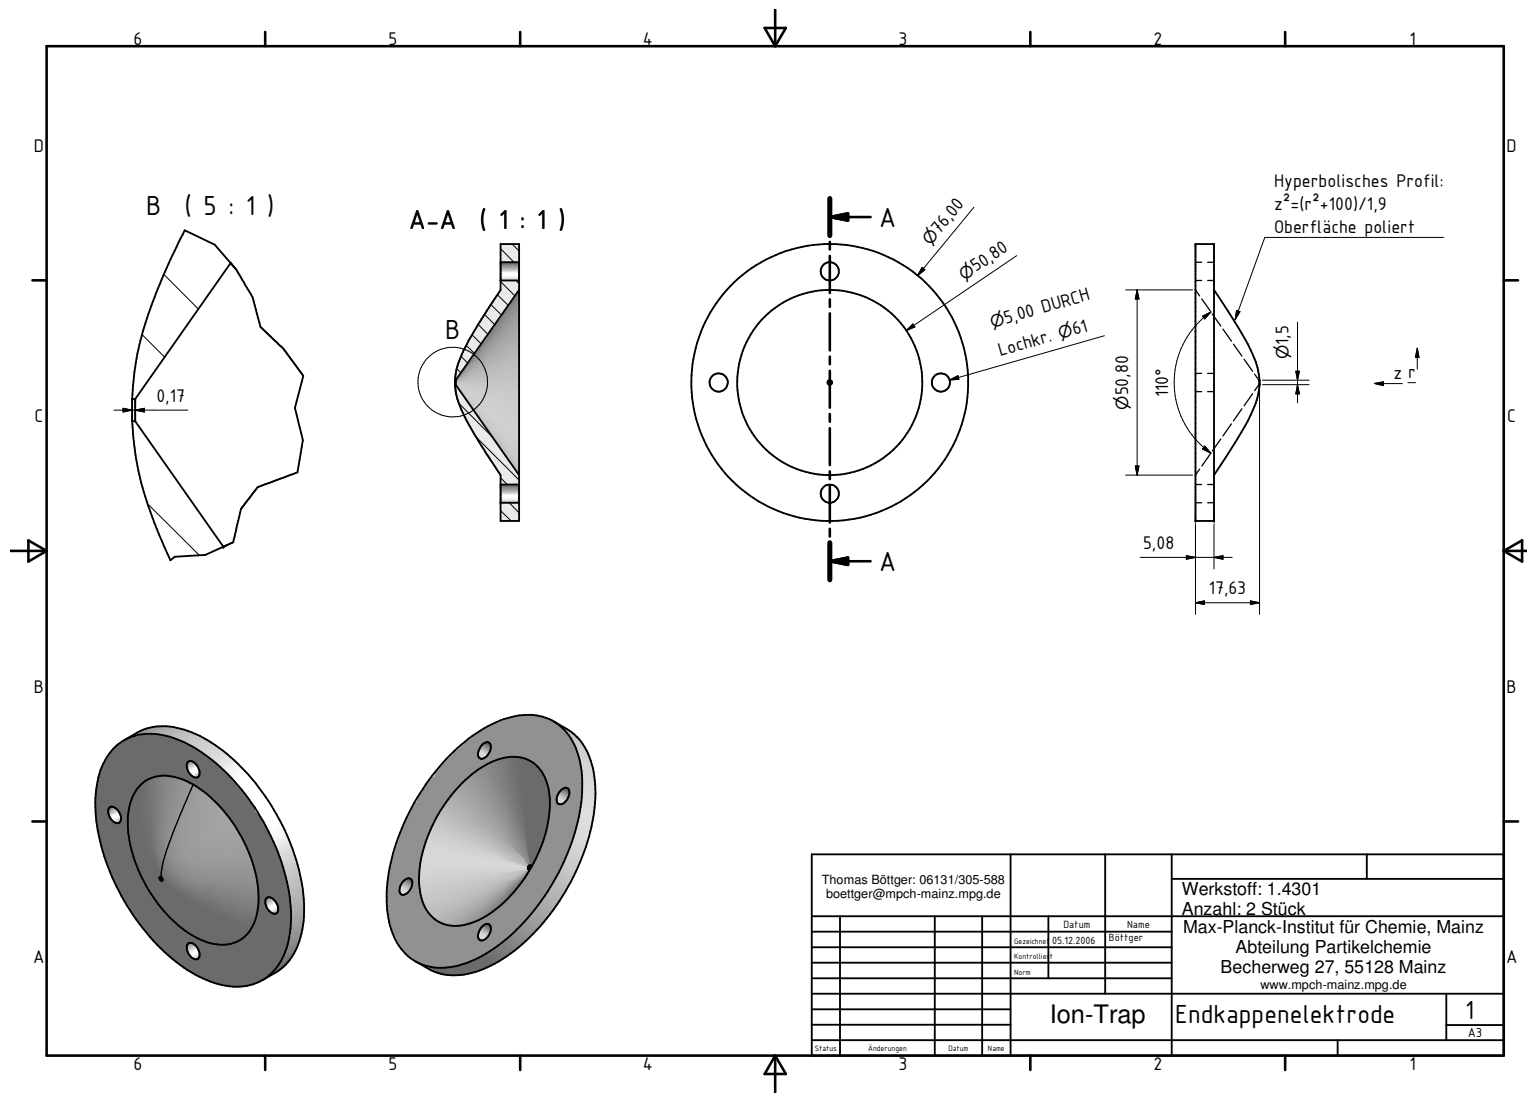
Technische Zeichnung der Endkappenelektroden.
